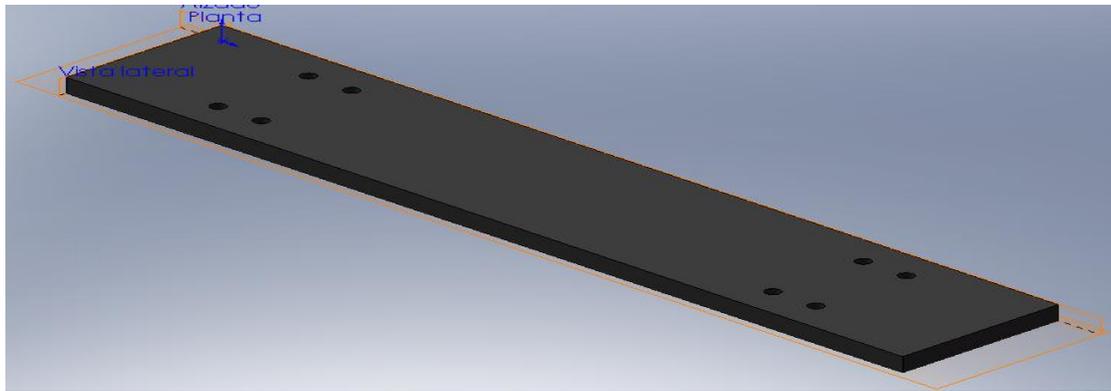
Vistas del soporte para las vigas del cilindro neumático inferior. Fuente autor
